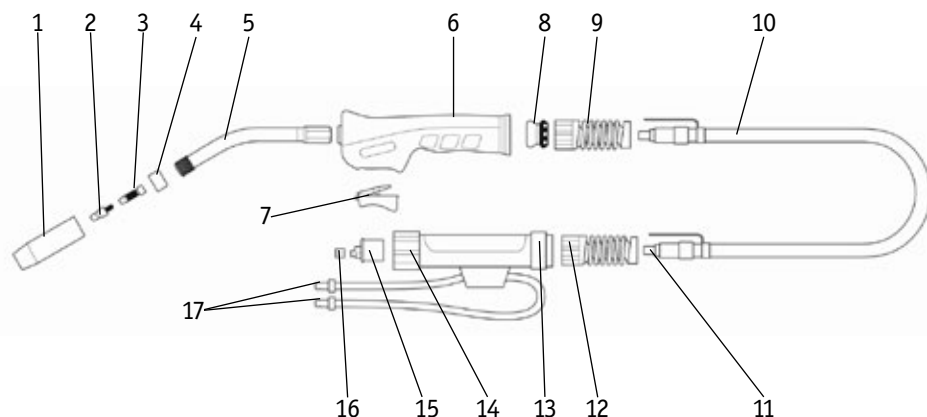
Схема горелки для MIG сварки.
